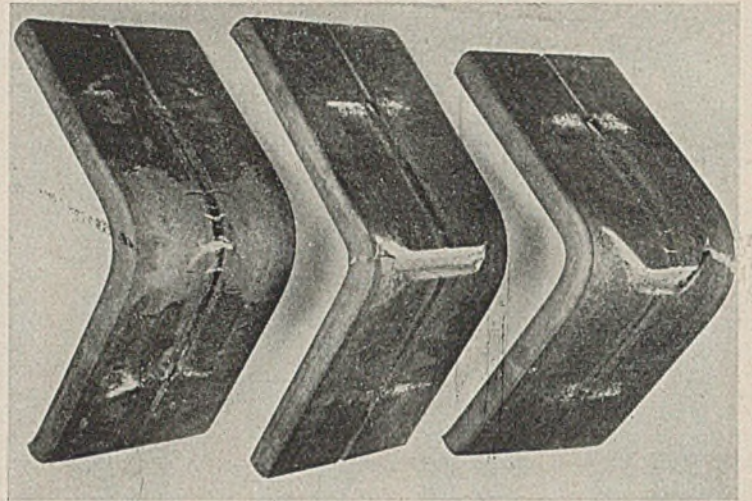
Schweißraupenbiegeprobe, St 48, 30 mm, Anlieferung.
